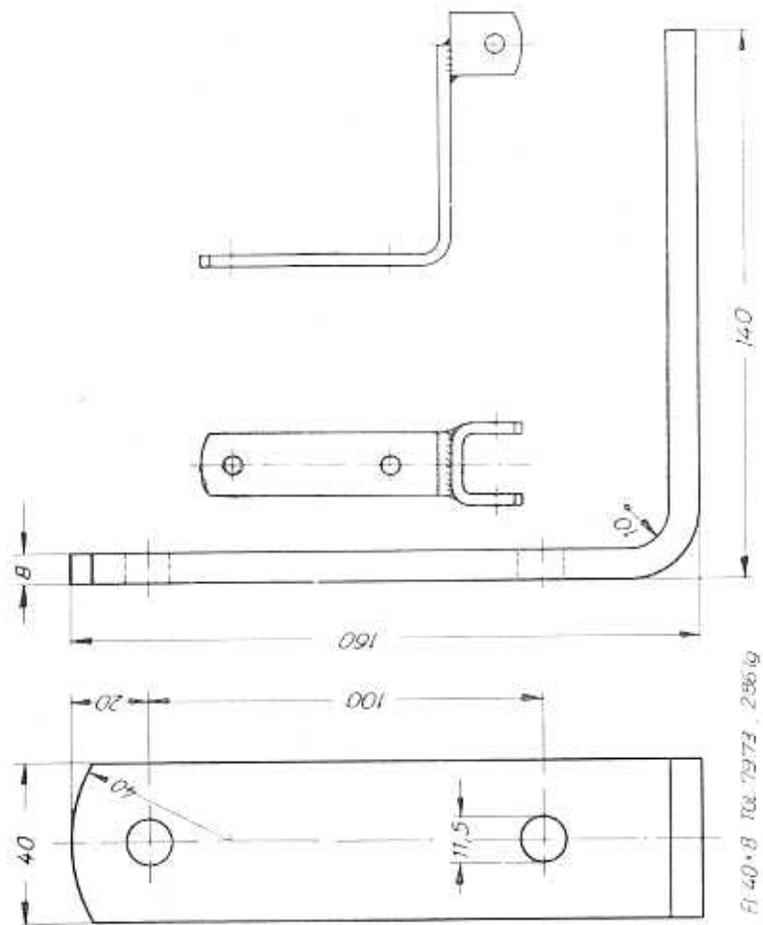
Haltebügel zum MT5 3, geschweißt
